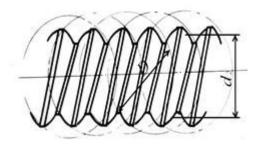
Резьбовой ролик: d_2 — средний диаметр резьбы; D_W — приведенный диаметр резьбы
